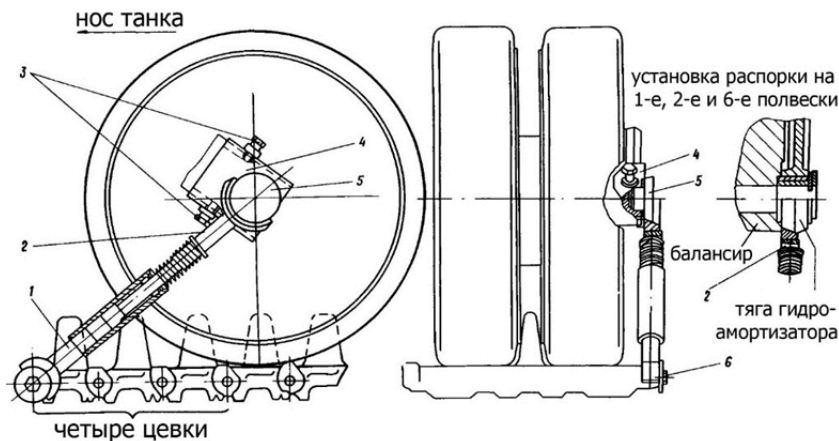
Установка приспособления для замены опорных катков без рассоединения гусениц:
